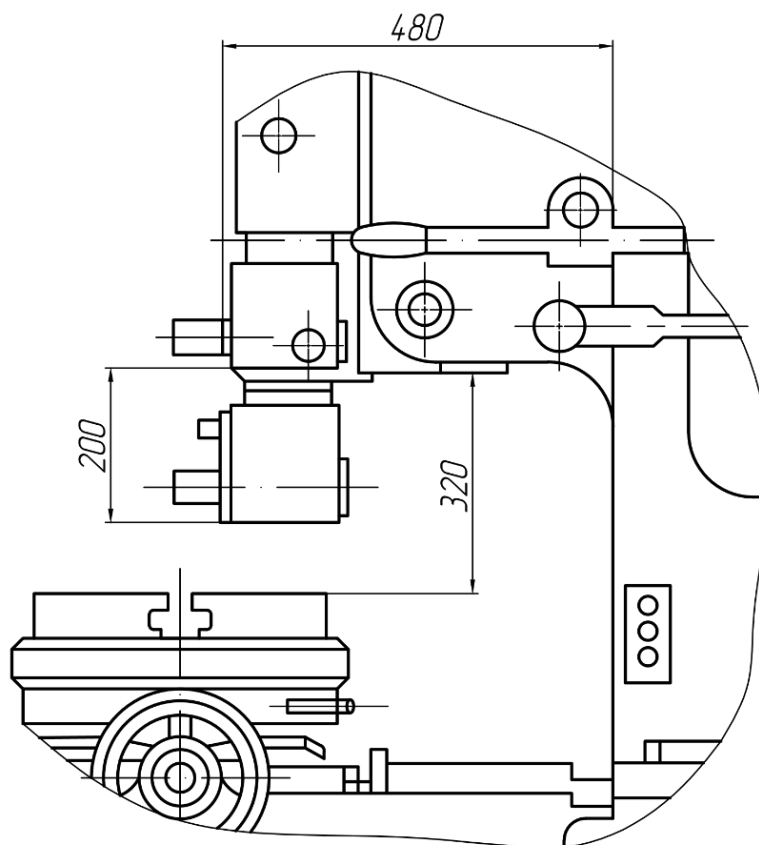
Схема габаритних розмірів робочого столу довбального верстату
